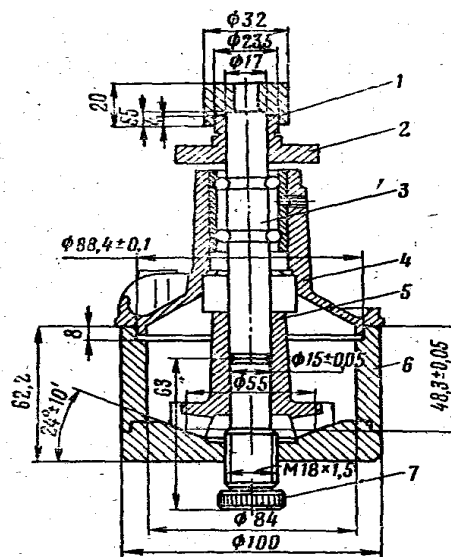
Приспособление А.60430 для напрессовки на валик крыльчатки насоса:
